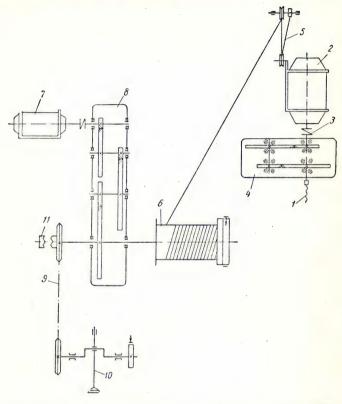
Кинематическая схема буровой установки БС-110/25м
